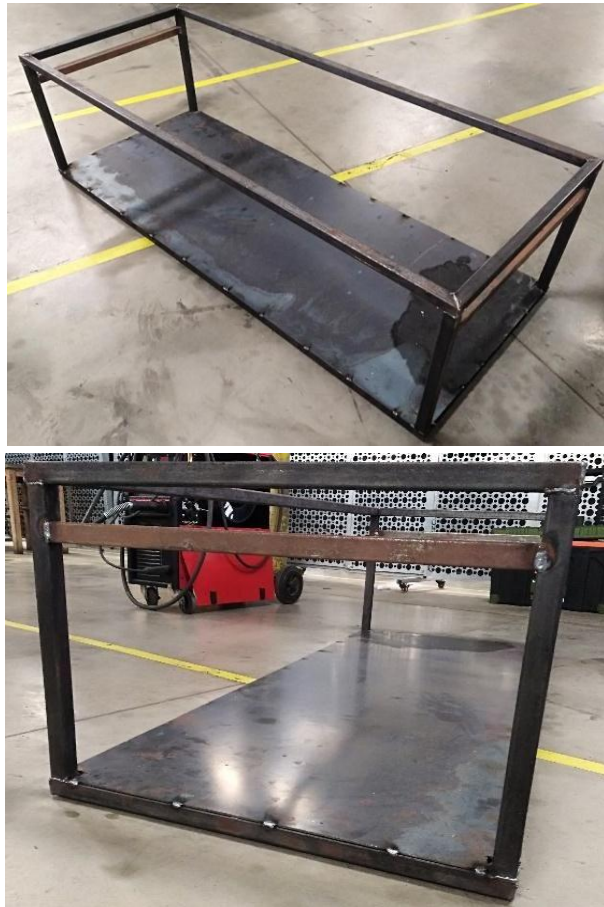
Ensamble de la estructura y la lámina de la base del equipo.
